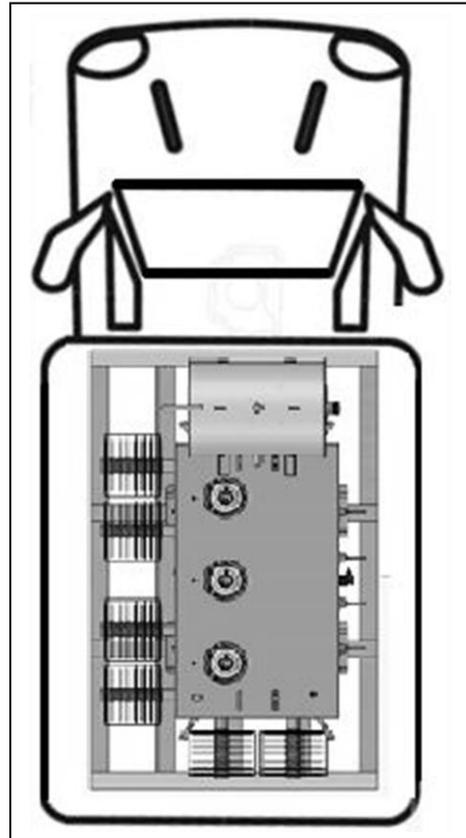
Tanque conservador (de expansión) al lado de la cabina
